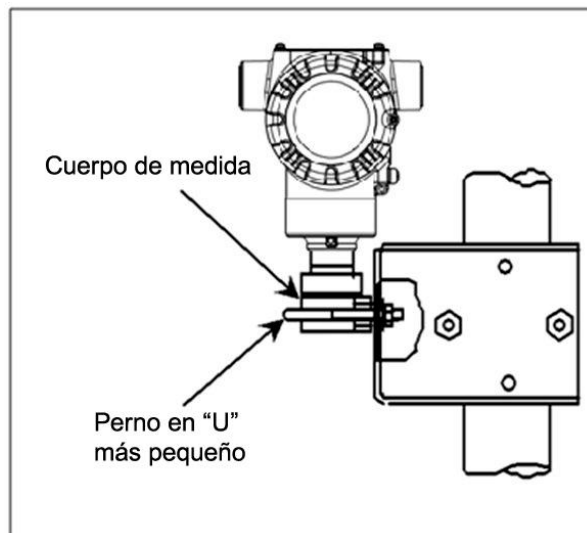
Soporte de montaje en ángulo fijado a una tubería horizontal o vertical
